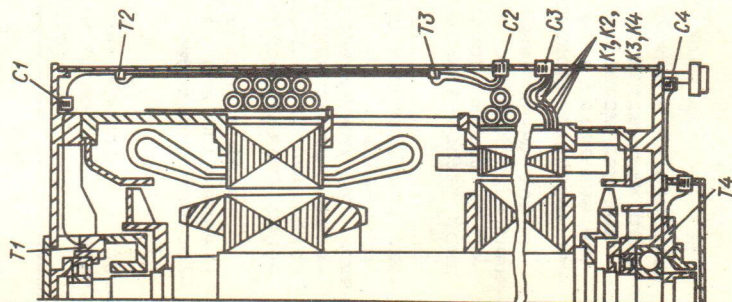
Схема расположения катушек для контроля воздушного зазора генератора преобразователей /вид сверху/:
